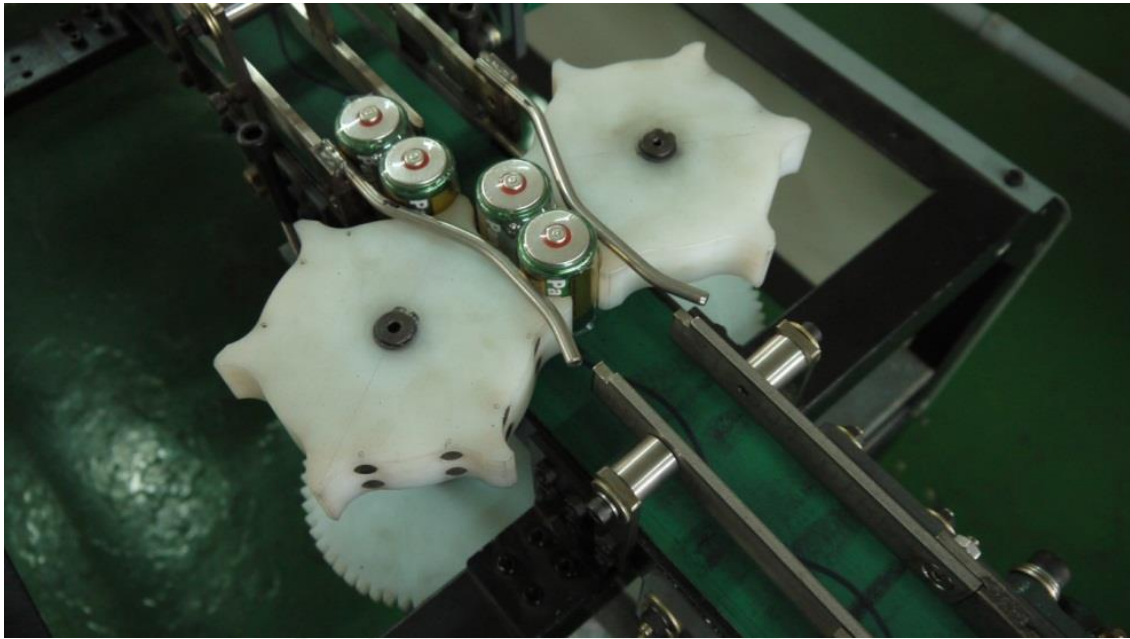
Pilas atravesando un par de estrellas divisoras 1-1
